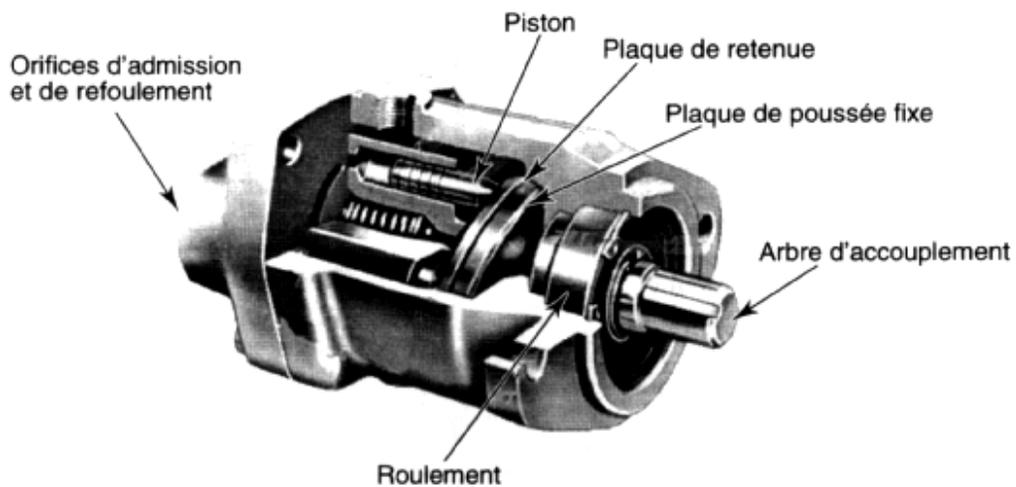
Moteur à pistons axiaux à cylindrée fixe
